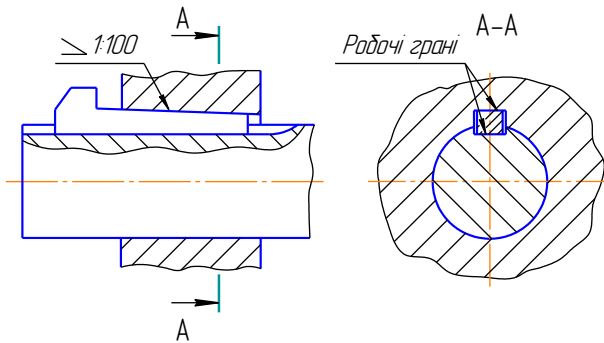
Конструкція шпонкового з'єднання з клинвою шпонкою
